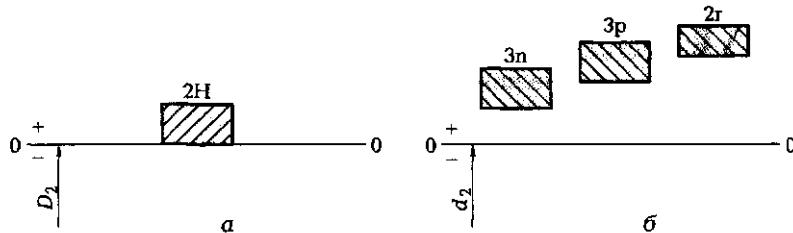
Расположение полей допусков резьбы с натягом для гнезд (а) и шпилек (б):
